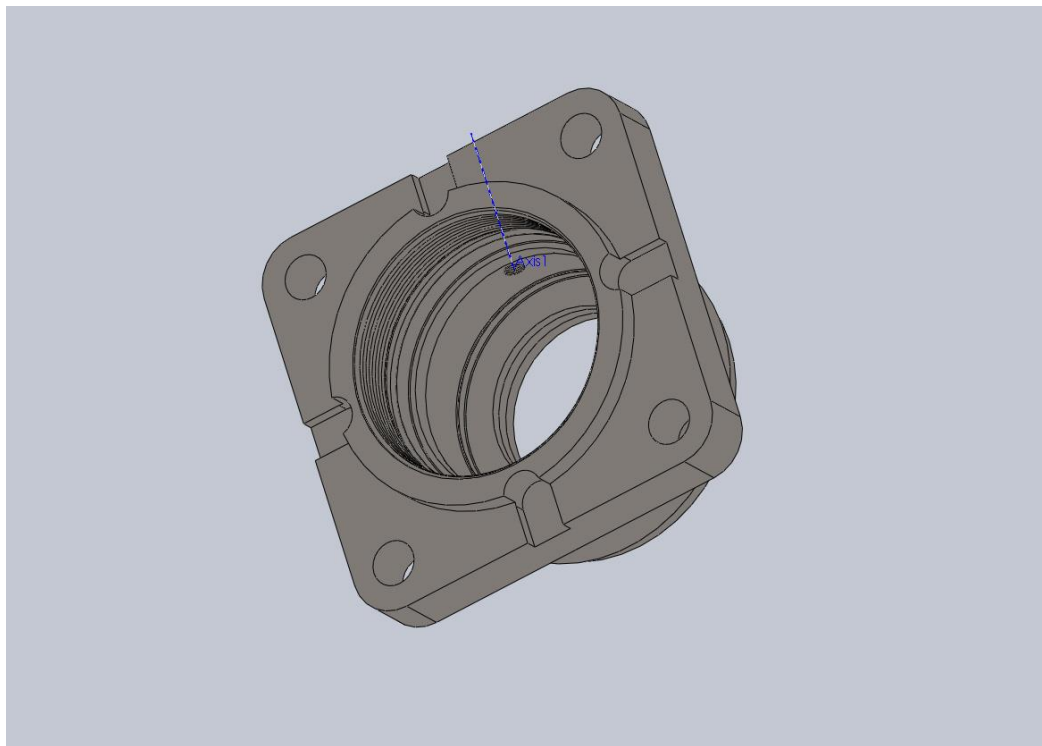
Ескіз деталі «Головка ІА. 11072-400ЛСБ» з номерами поверхнь
